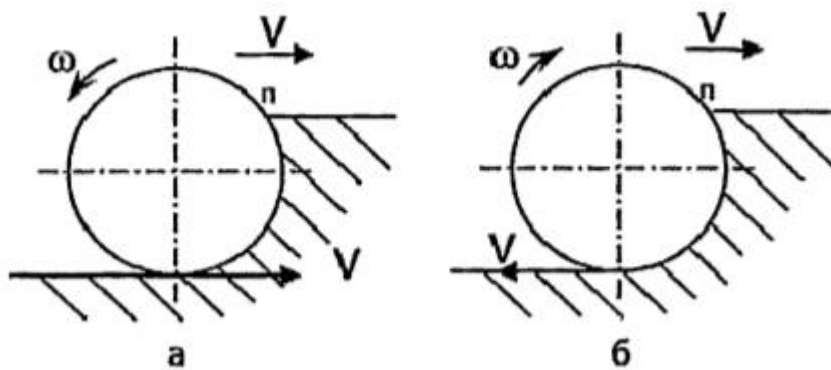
Режими роботи поздовжньо-осьової коронки: а - попутне фрезерування; б - зустрічне фрезерування
